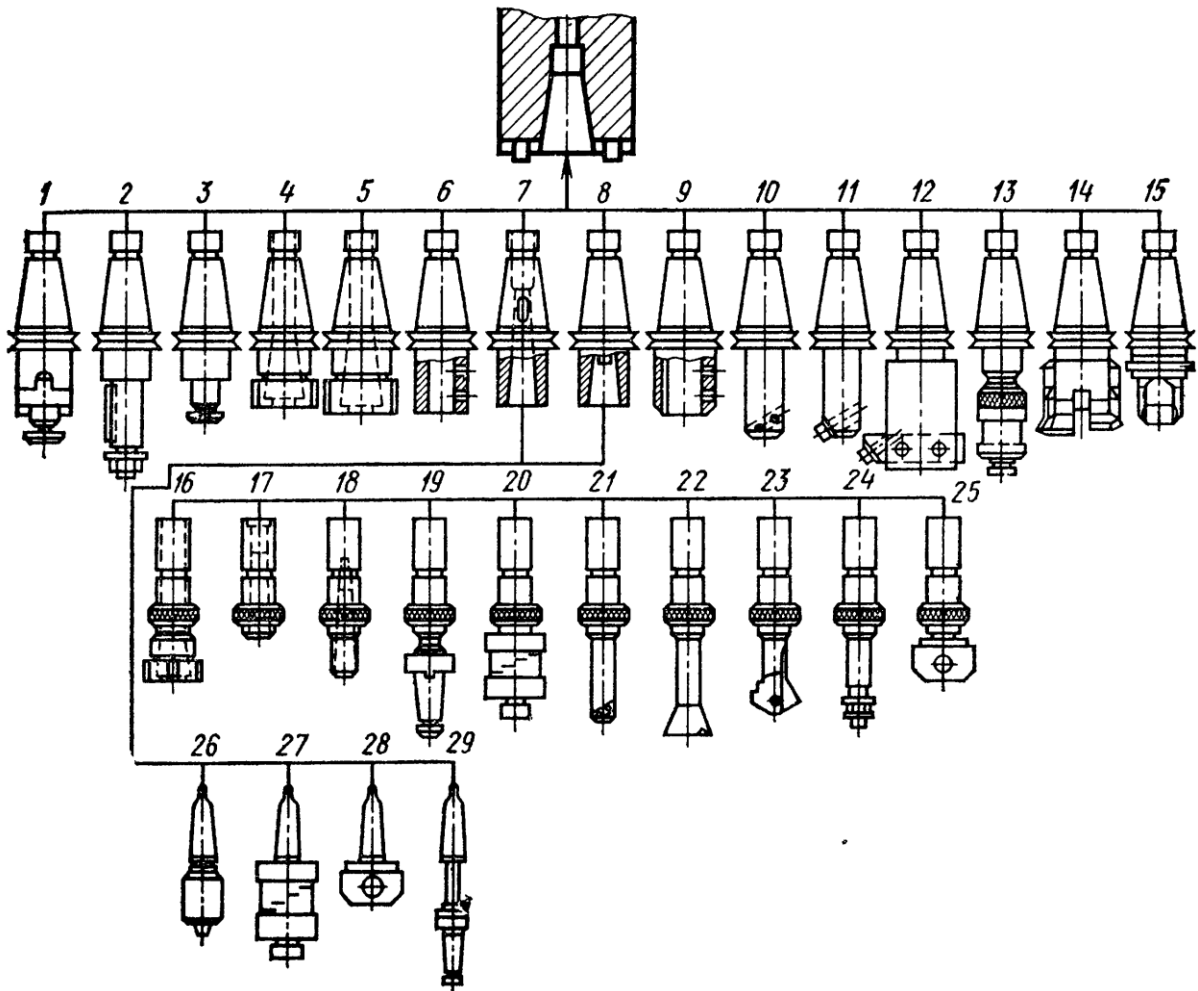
Система допоміжного інструменту для верстатів з ЧПК, обробних центрів і ГВС, верстатів свердильно-розточний і фрезерної груп
